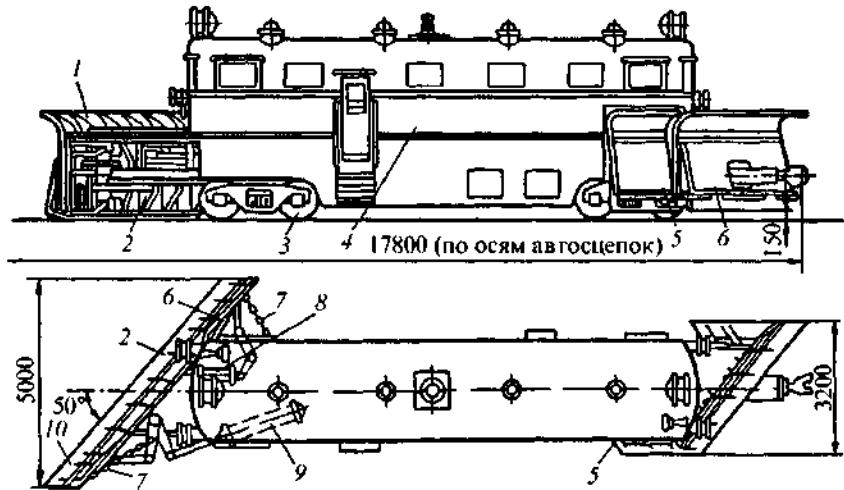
Двухблочный плужный снегоочиститель СДП: 1 — козырек; 2 — передний щит; 3 — тележка; 4 — кузов; 5, 6 — боковые крылья; 7 — цепная растяжка; 8, 9 — пневмоцилиндры поворота крыльев; 10 — угловое крыло
